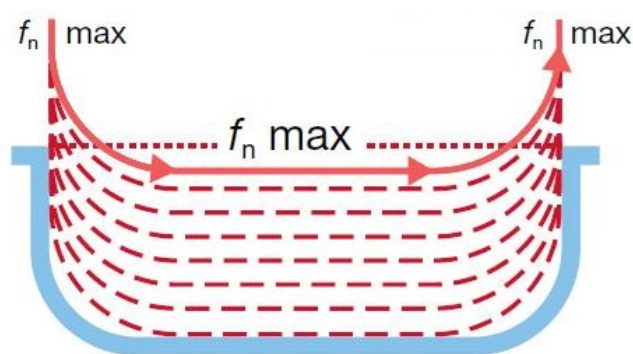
Схеми чорнкової токарної обробки зі збільшеною подачею
